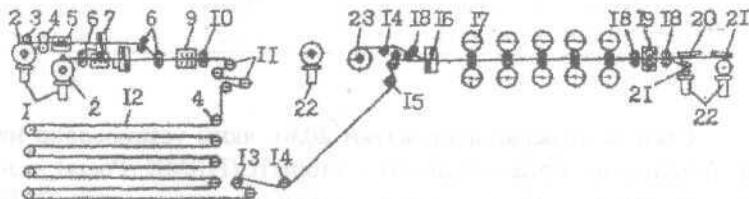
Схема розташування обладнання п'ятикліткового стана безперервної прокатки 2030: 1-рулонний візок; 2-розмотувачі; 3-притискувальний ролик; 4-8-тягнучі ролики; 5-правильна машина; 6-стіл; 7-ножиці; 9-зварна машина; 10, 11-натяжні станції; 12-петльовий накопичувач; 14-направляючі ролики; 16-ножиці; 17-кліті; 19-ножиці; 20-магнітний транспортер; 21-моталка; 22-рулонний візок; 23-розмотувач.
